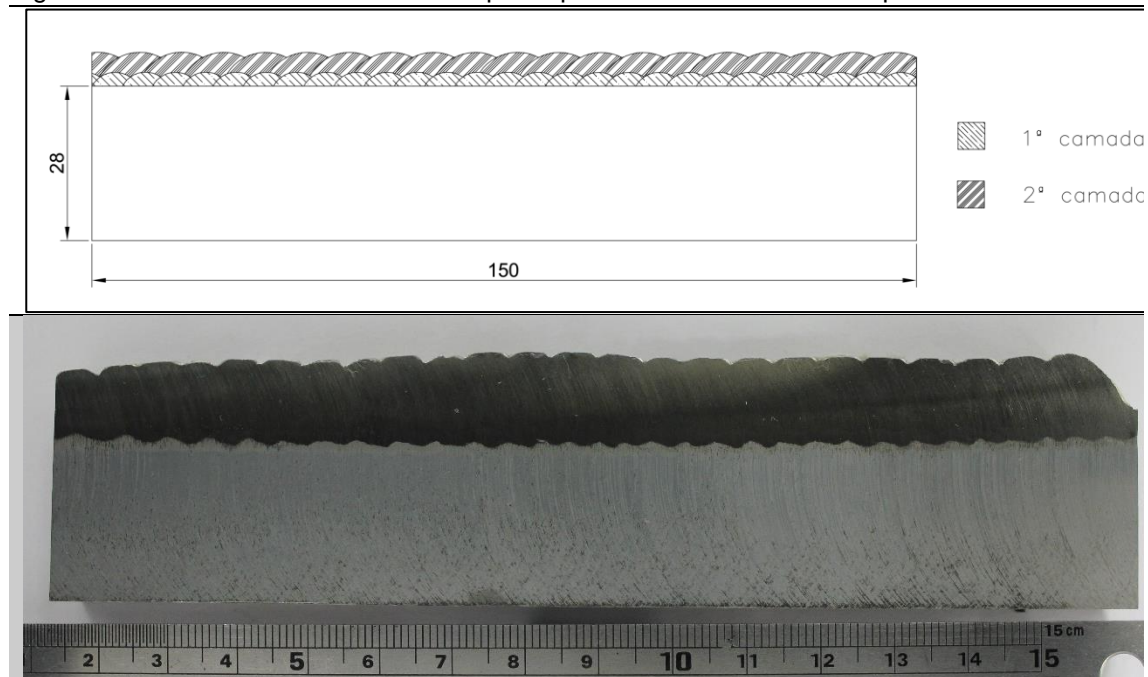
Formato e dimensões do corpo de prova de dobramento do reparo de parede.
